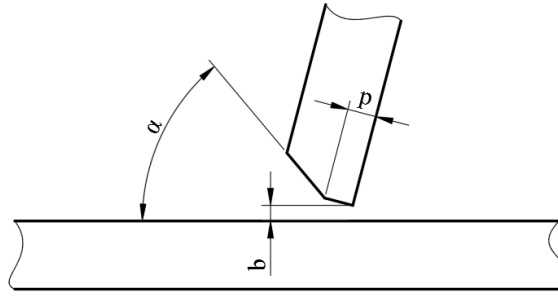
U 形肋角焊缝坡口加工以及组对精度示意图
